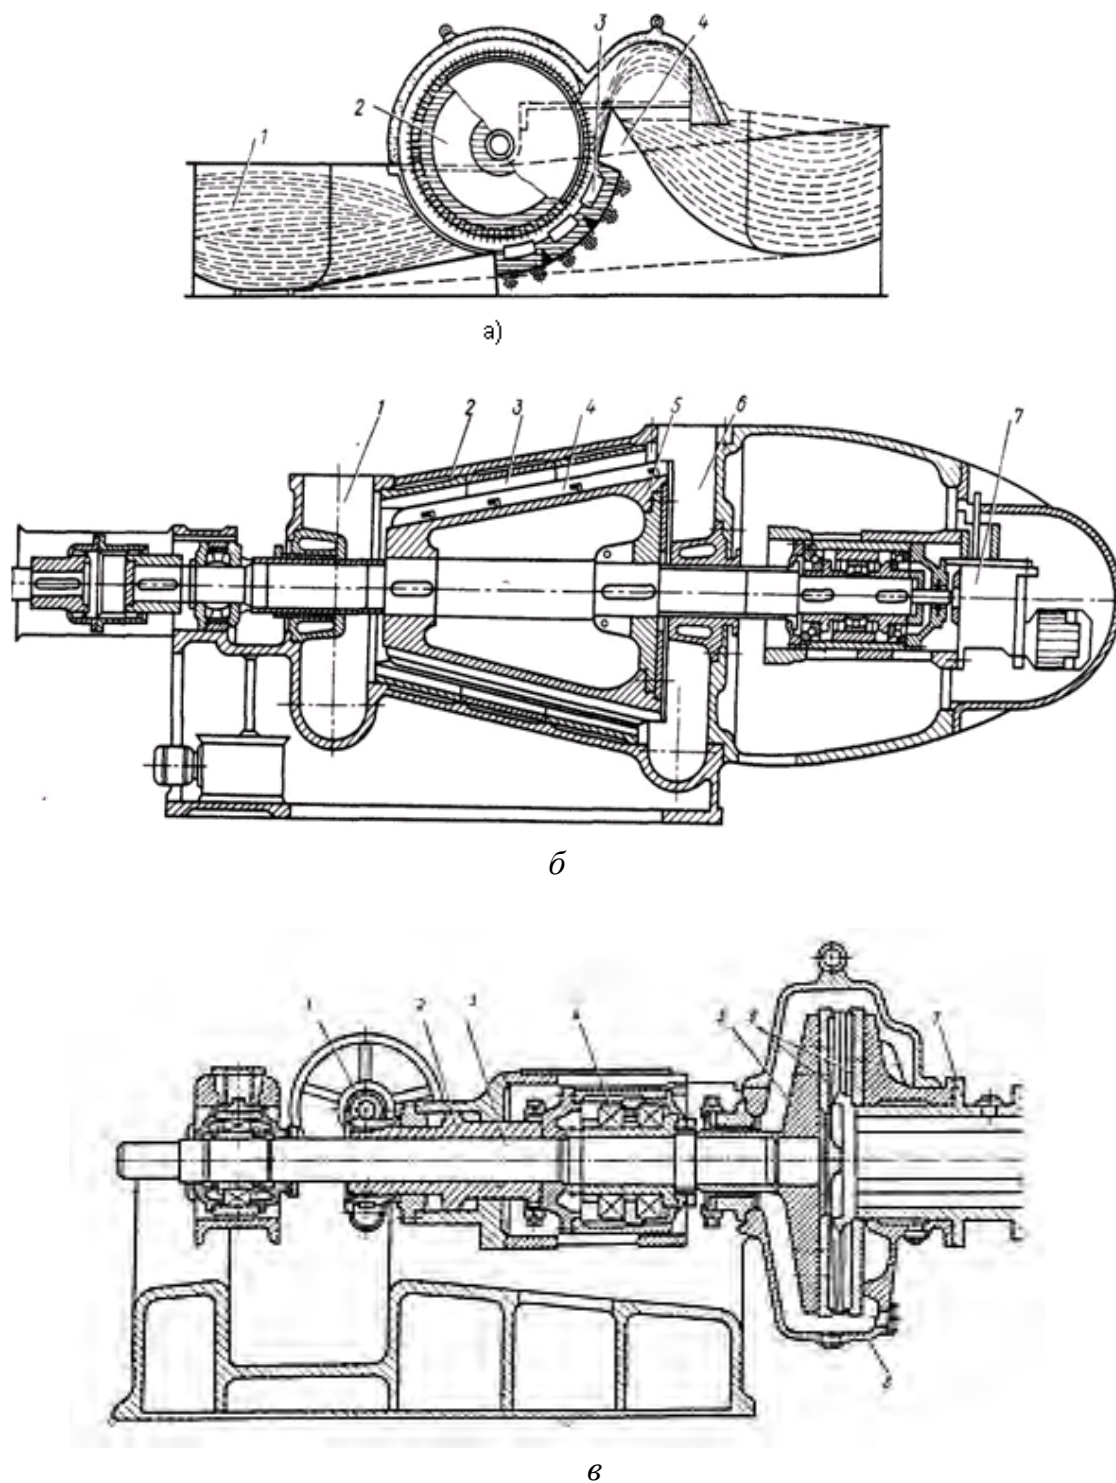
Основные типы ножевых размалывающих машин: *а* – ролл: 1 – ванна; 2 – ножевой барабан; 3 – планка с ножами; 4 – горка; *б* – коническая мельница: 1 – входная полость; 2 – корпус статора; 3, 4 – ножи статора и ротора; 5 – кольцевая стяжка для крепления ножей ротора; 6 – выходная полость; 7 – механизм присадки; *в* – дисковая мельница: 1 – механизм присадки; 2 – гидроцилиндр механизма присадки; 3 – вал; 4 – подшипники; 5 – диск; 6 – ножевая гарнитура ротора и статора; 7 – входной патрубок; 8 – размольная камера
